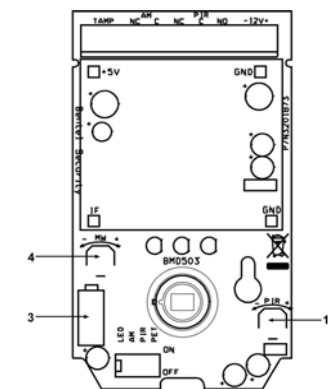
Parti della scheda elettronica I PCB layout Componentes del la tarjeta I Composants de la carte
